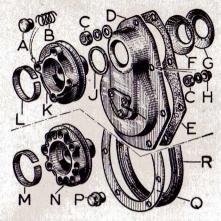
Fig. B. — Détail du montage de la poulie et du couvre-engrenage
